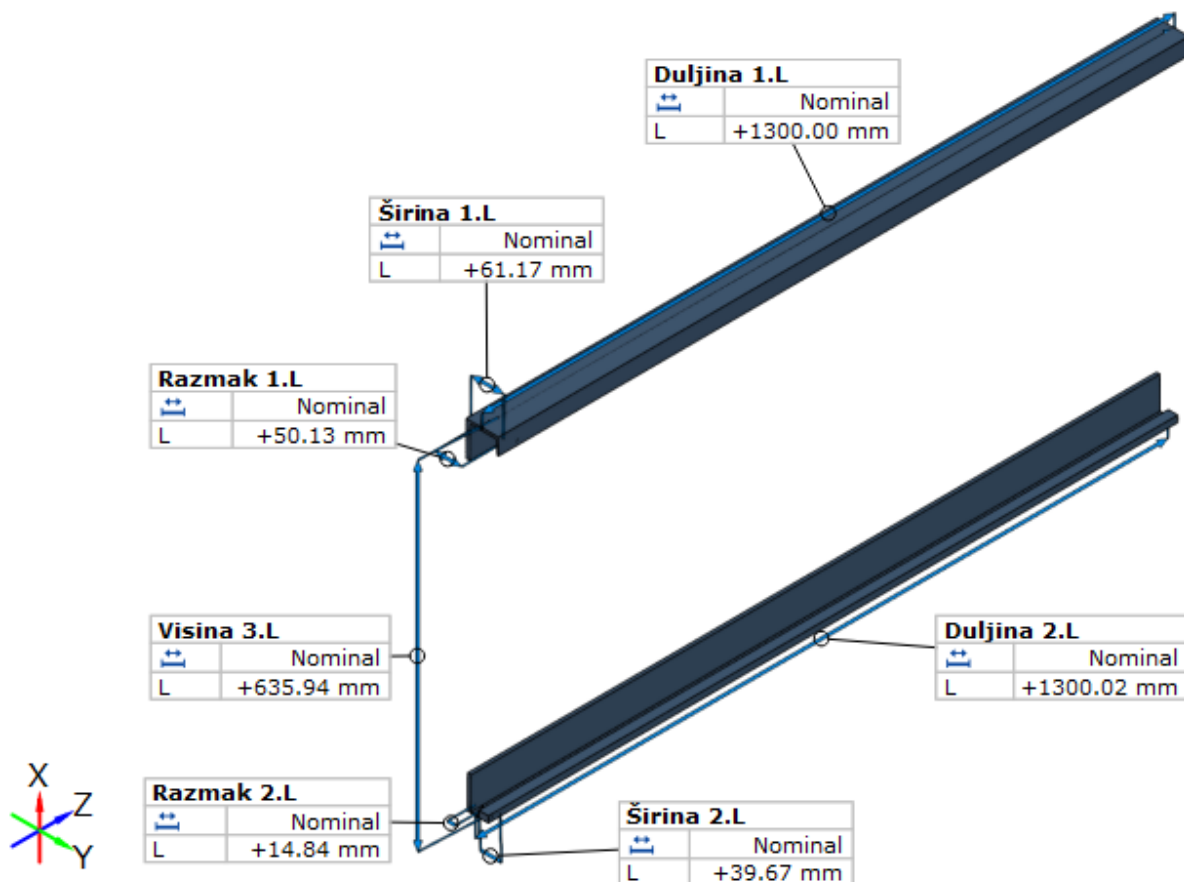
Dimenzije glavnih značajki rekonstruiranog CAD modela manipulatora
